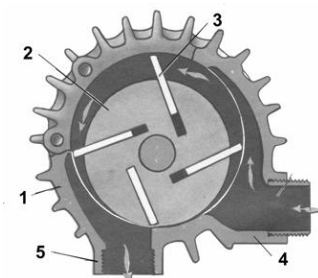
Разрез ротационного лопаточного вакуумного насоса типа УВД: 1 – корпус; 2 – ротор; 3 – лопатка; 4 – всасывающий патрубок; 5 – выхлопной патрубок
